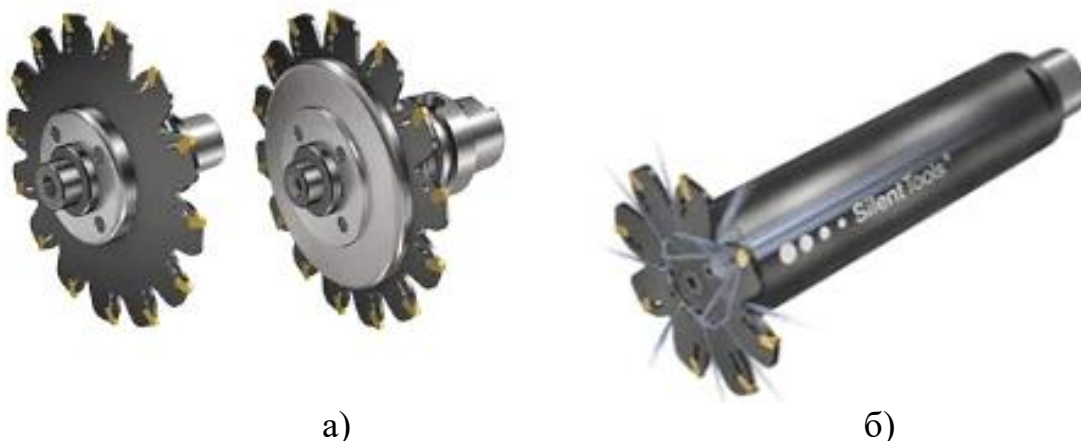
Відрізнi фрези дискового типу а) та з оправкою б) [12]
